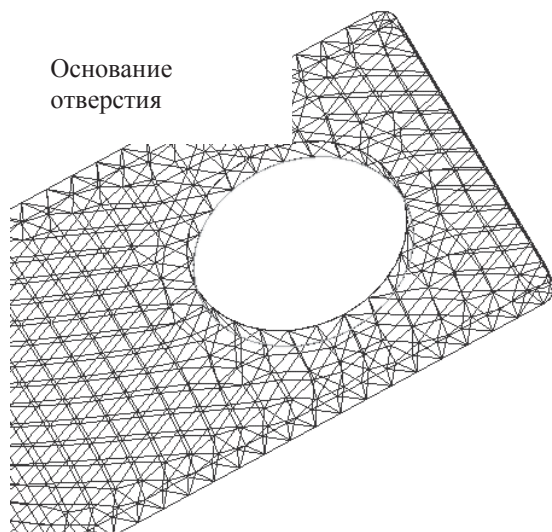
Общий вид зоны конструкции для приложения нагрузки
